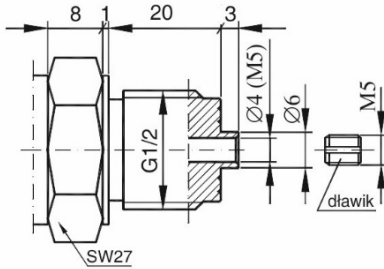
а. Штуцер типа G1/2 с резьбой G1/2"
